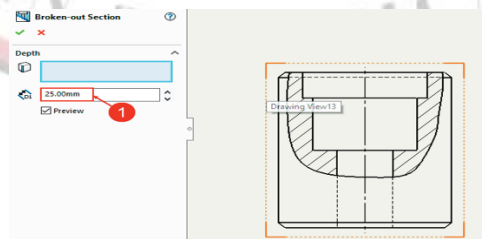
การเรียกใช้คำสั่ง Break-out Section
